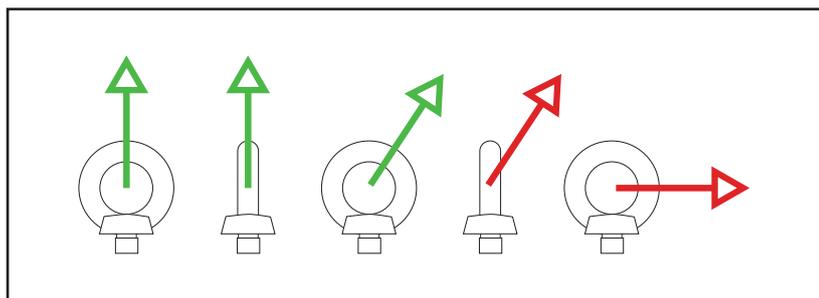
Zulässige Belastungsrichtungen für Ringschrauben
